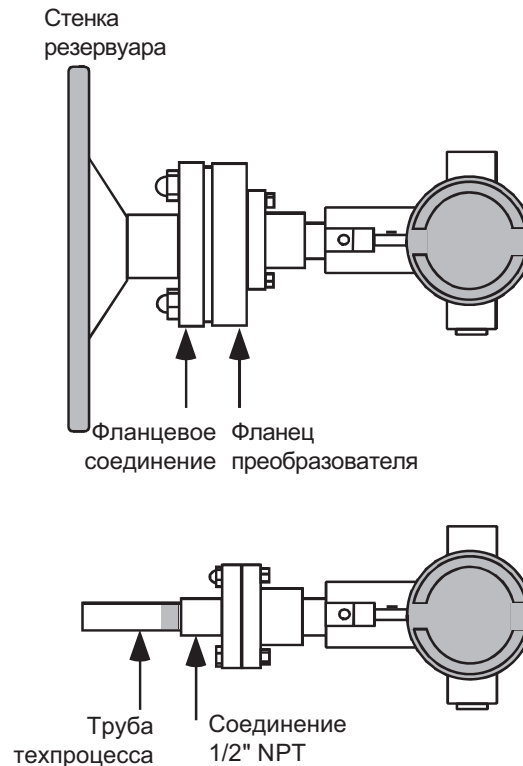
Типовой монтаж преобразователя с фланцевым креплением и с креплением на трубу
